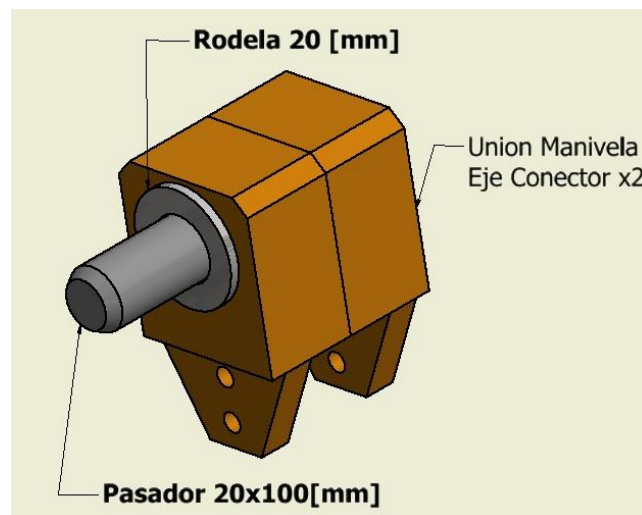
DIMENSIONES SOPORTE EJE CONECTOR
